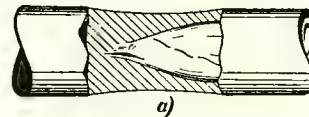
Образование трещин при неправильной прошивке заготовки труб.
